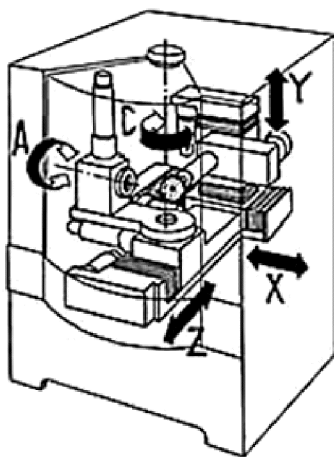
Компонировочная схема 5-ти координатного шлифовальнозаточного центра с ЧПУ
